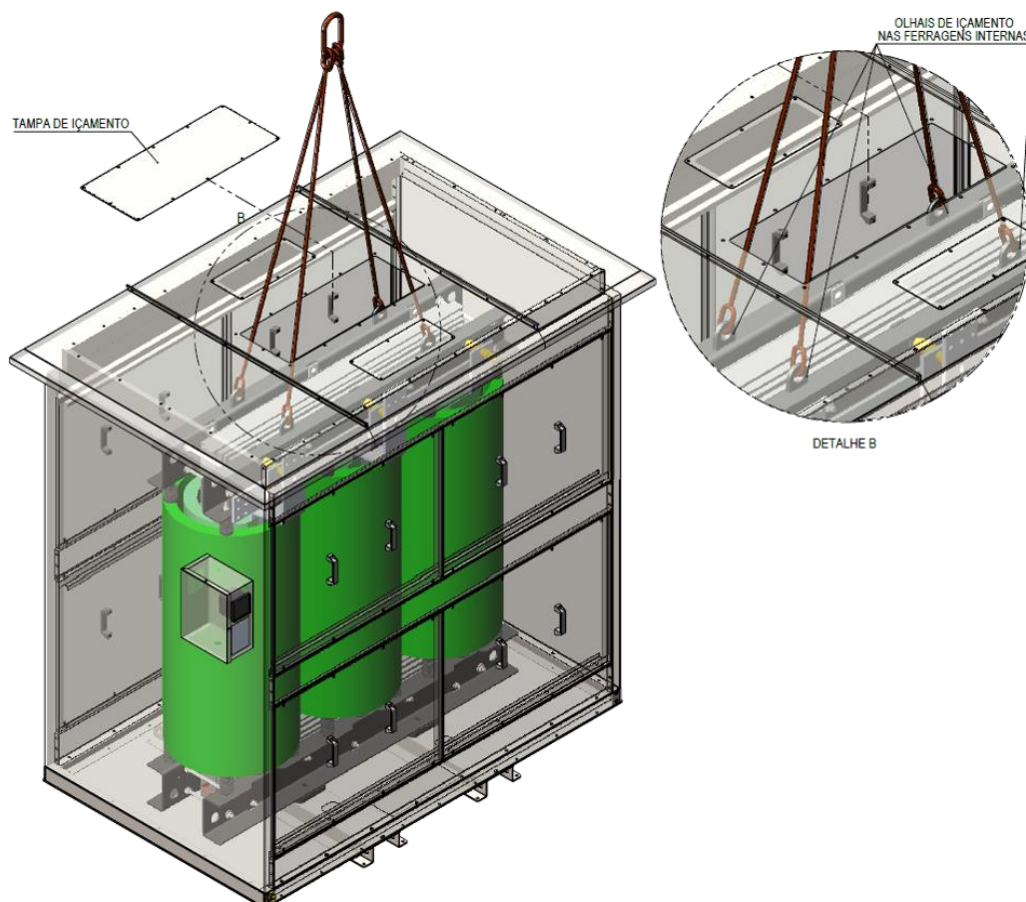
Içamento do conjunto (transformador e invólucro de proteção)
